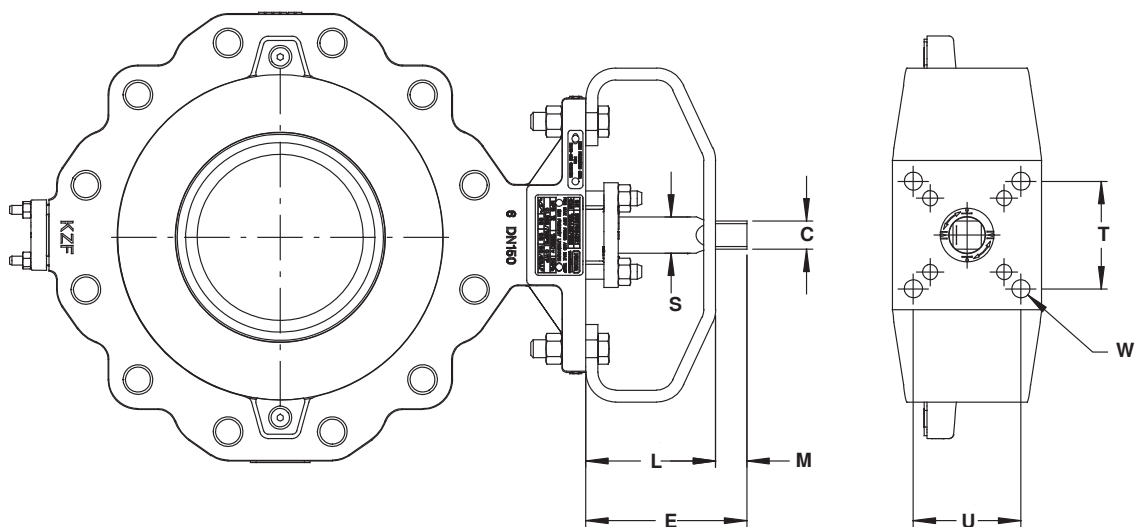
Габаритные размеры затвора Fisher 8580 с дополнительным монтажным кронштейном под квадратный вал
